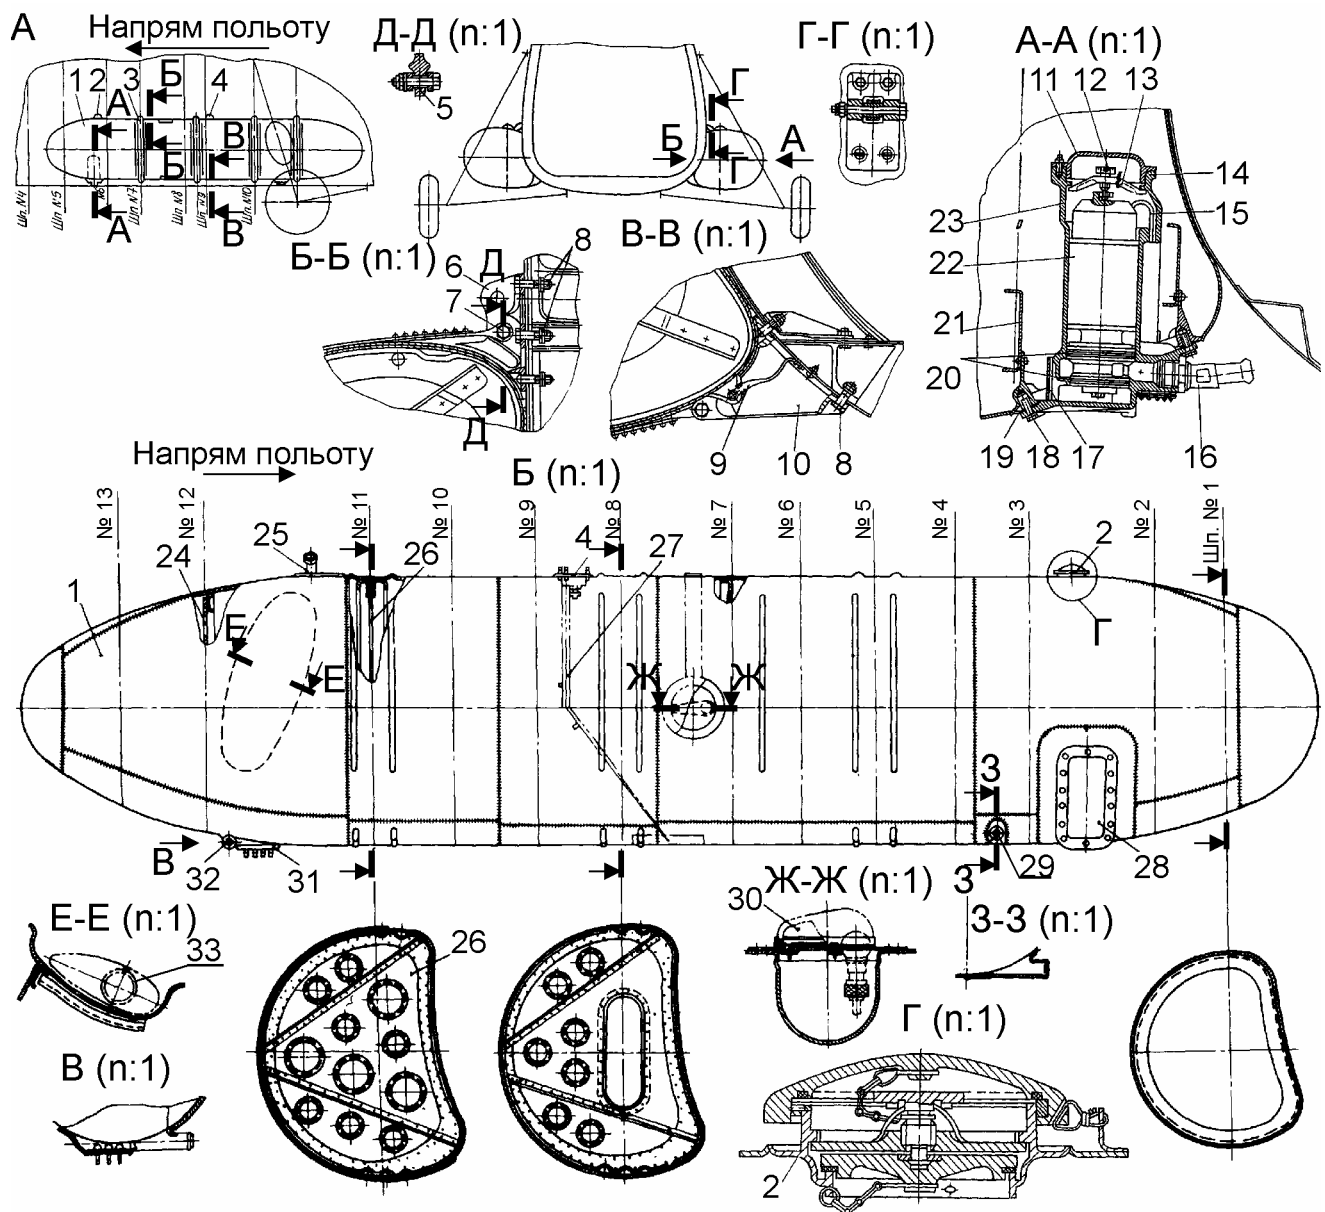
Конструкція ППБ вертольота (Ми-8):
